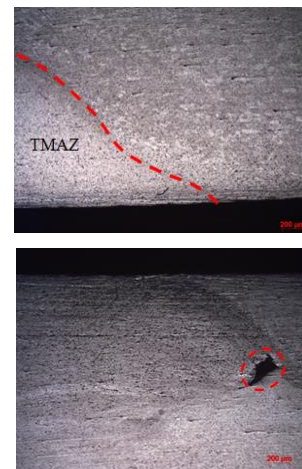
Soldadura da amostra FSW F1: a) Zona termicamente afetada. b) Cordão de Soldadura.
